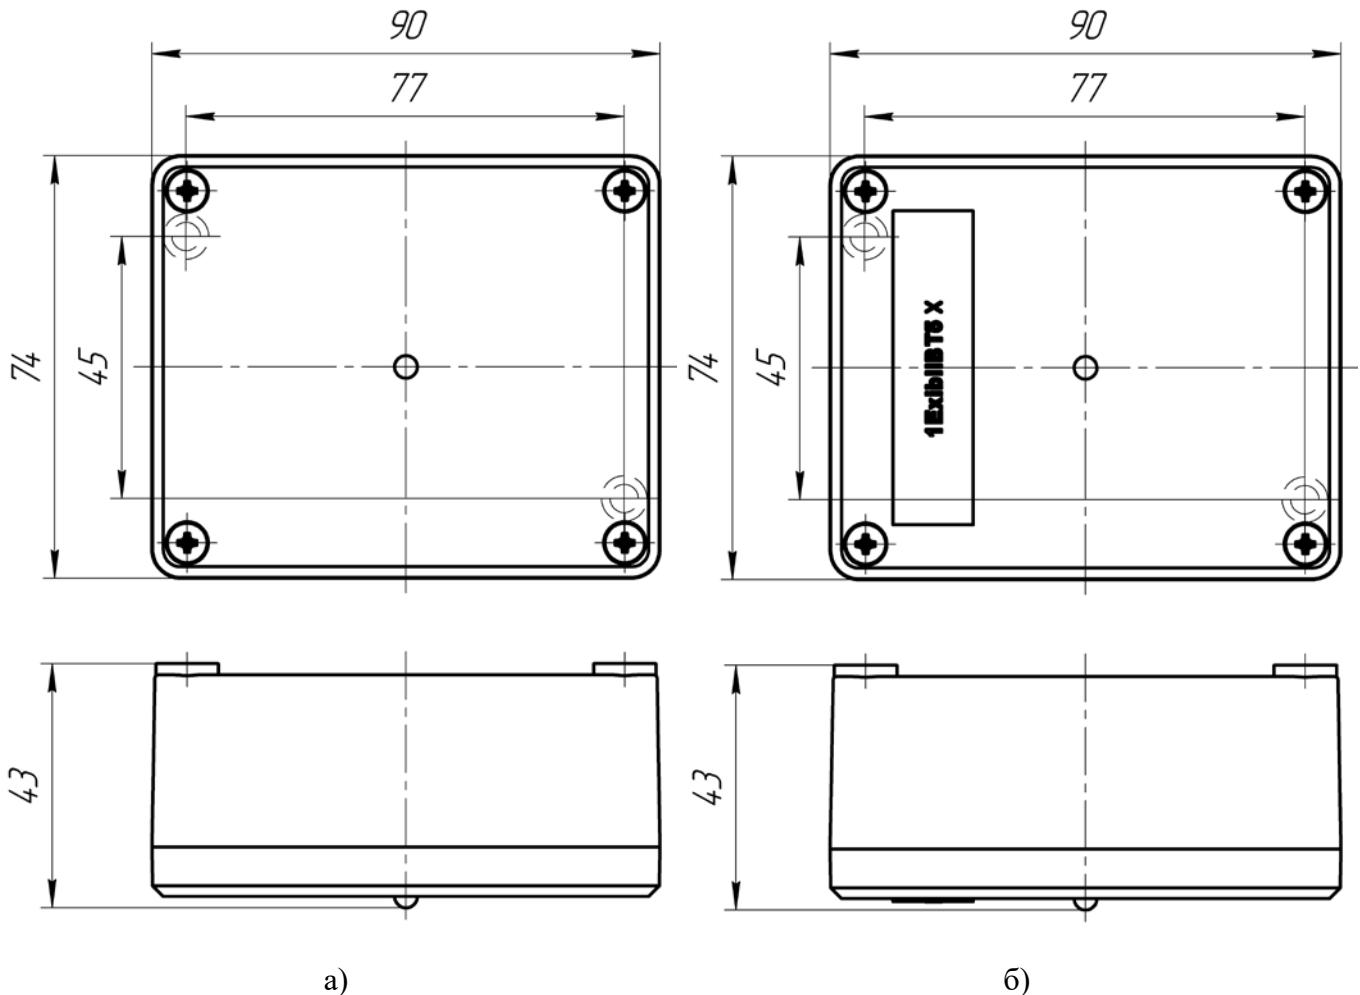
Внешний вид, габаритные и установочные размеры БСА (а) и БСА-В (б), размеры в мм.
